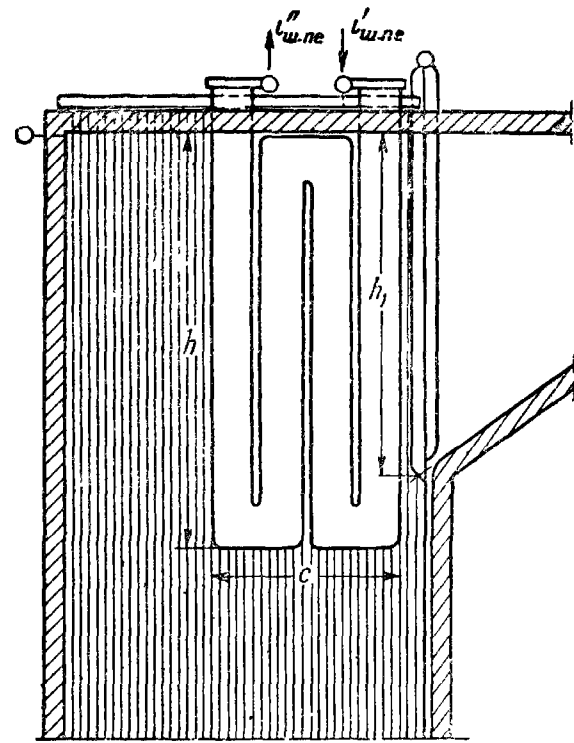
Эскиз размещения ширмового пароперегревателя в топке.
